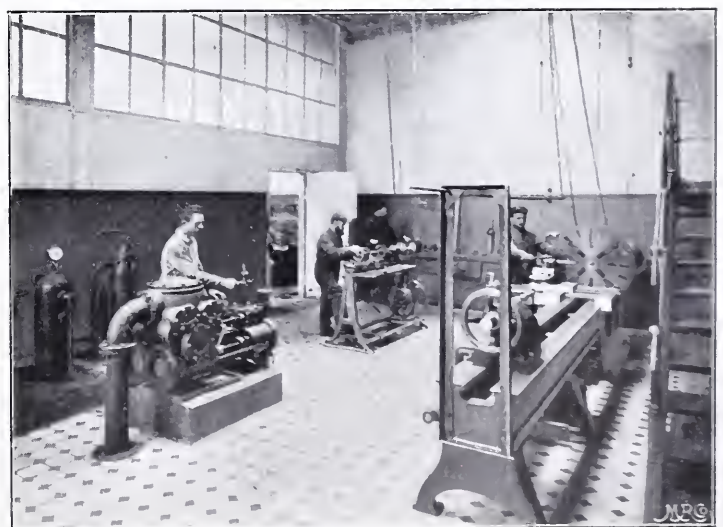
Worthingtonpumpe und Werkzeugmaschinen.
